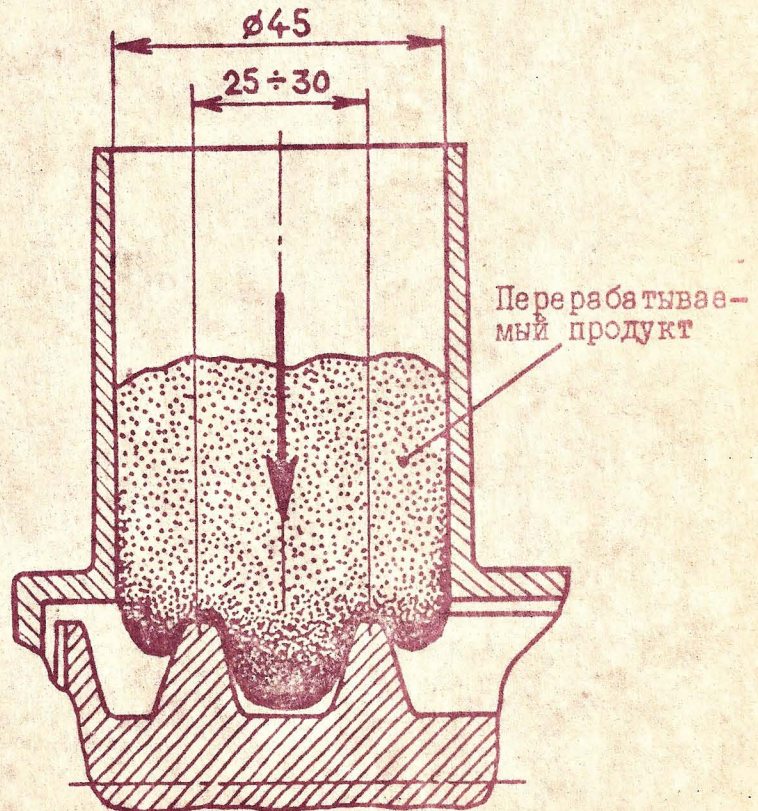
Захват перерабатываемого продукта витками шнека в задней части корпуса
